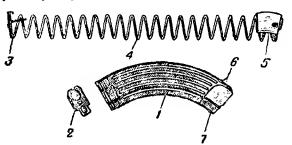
Коробчатый магазин: I — корпус; 2 — крышка; 3 — стопорная планка; 4 — пружина; 5 — поляватель; 6 — опорный выступ; 7 — зацеп
